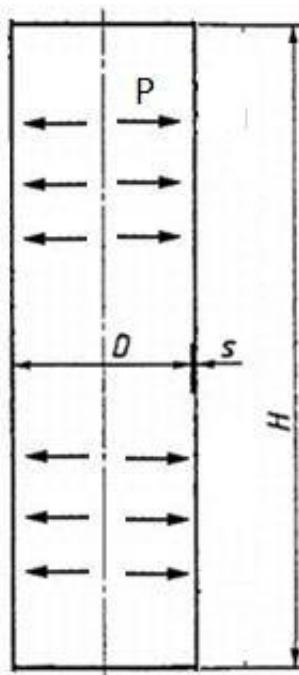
Розрахункова схема циліндричної частини колони
